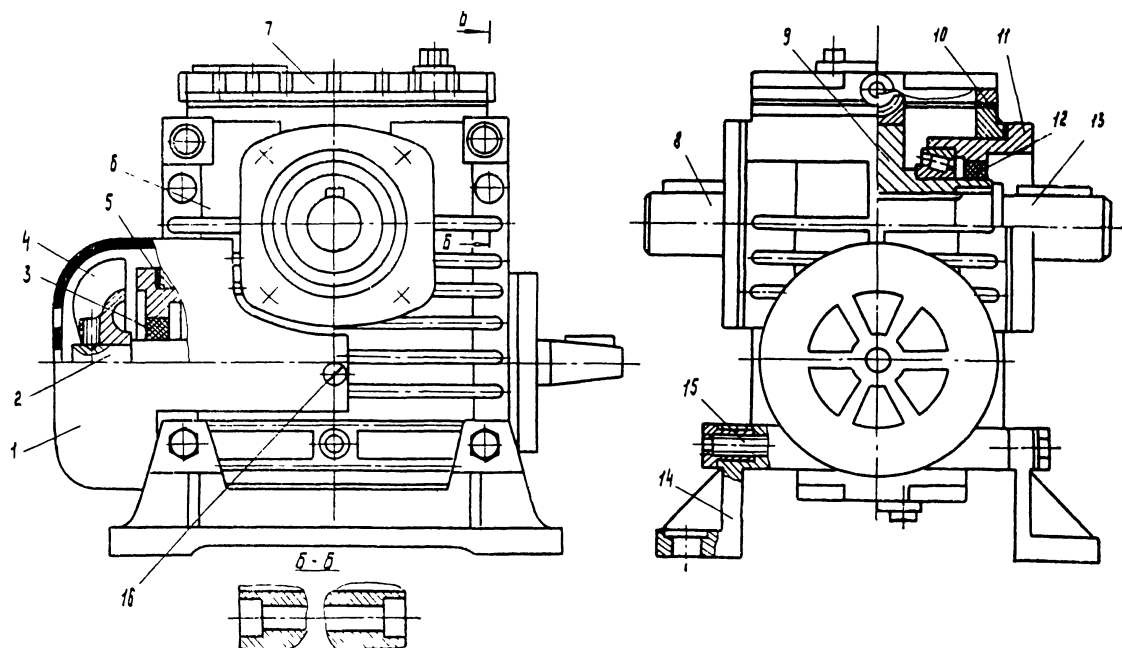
П7 Общий вид редуктора типоразмера Ч-80
